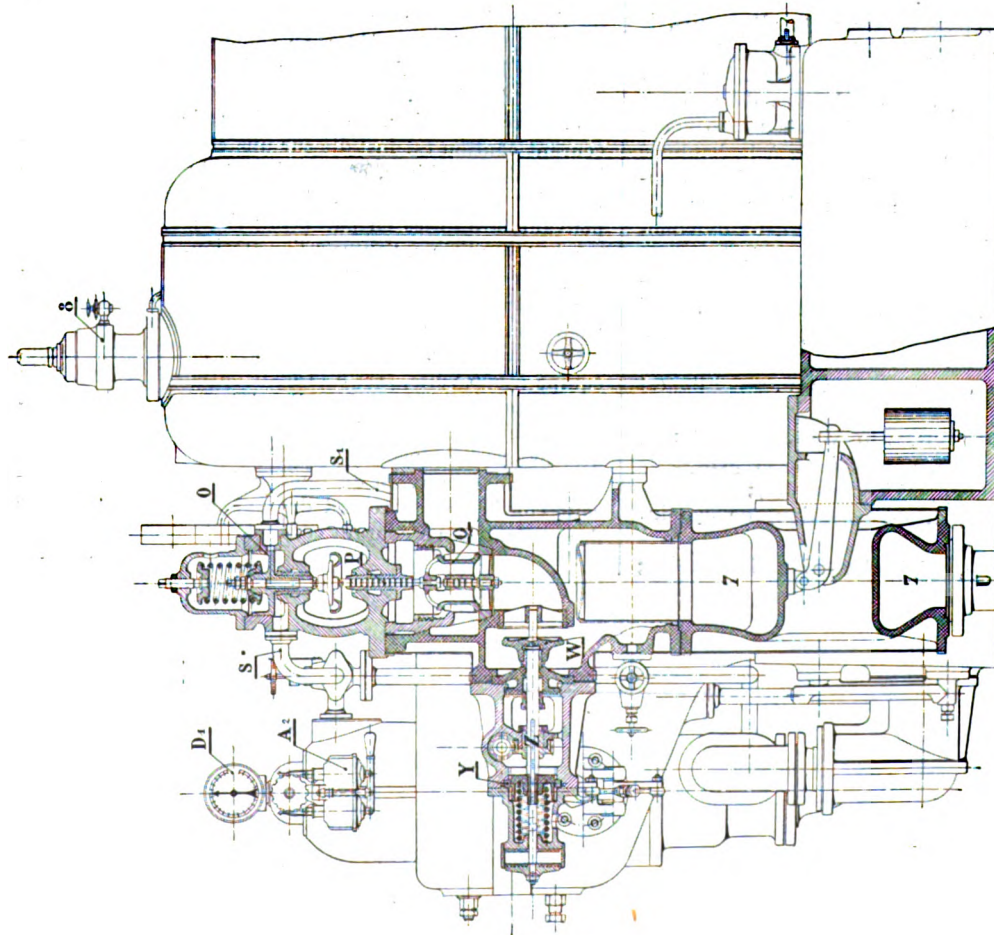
et 7. — Vue de côté, coupe par l'admission de vapeur et vue en bout, coupe par les organes de réglage.
